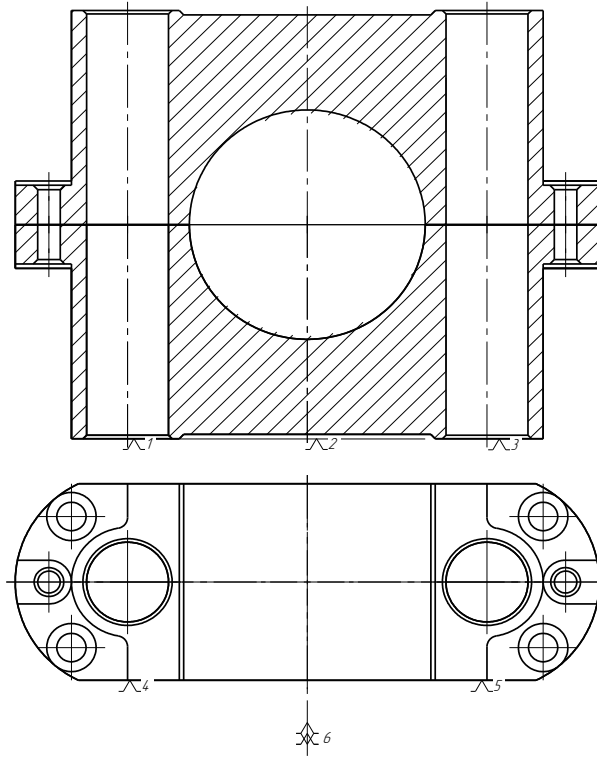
Теоретична схема базування корпусу в зборі
